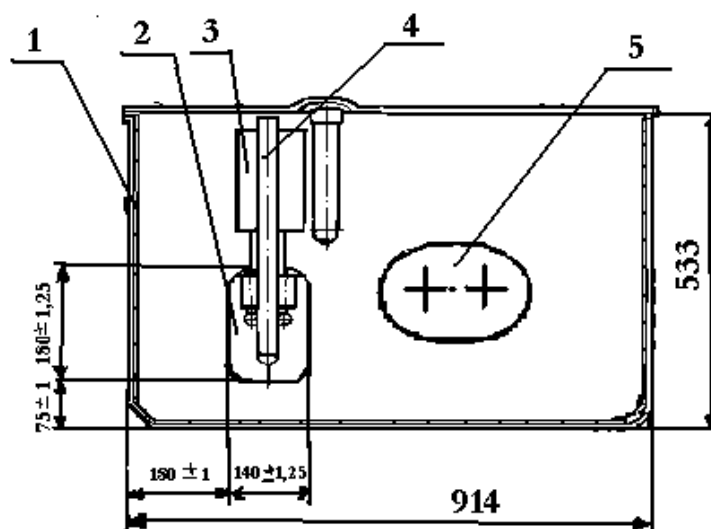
Пример установки запорного клапана в баке вагона: 1 - бак; 2 - коллектор; 3 - запорный клапан; 4 - переливная труба; 5 - люк
